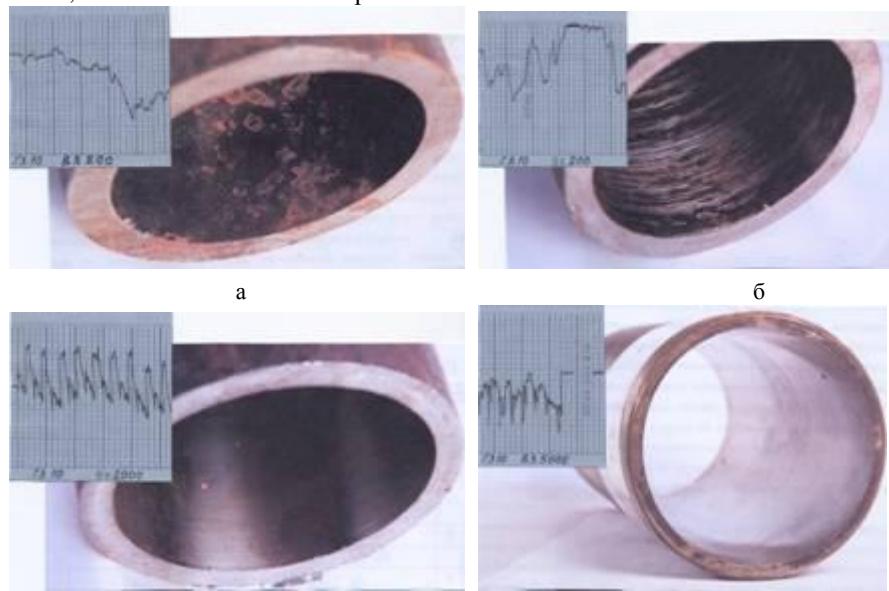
Стан та профілограми поверхні заготовки гільзи: а – в стані поставки; б – після чорнового розточування; в – після чистового розточування; г – після розкочування.
